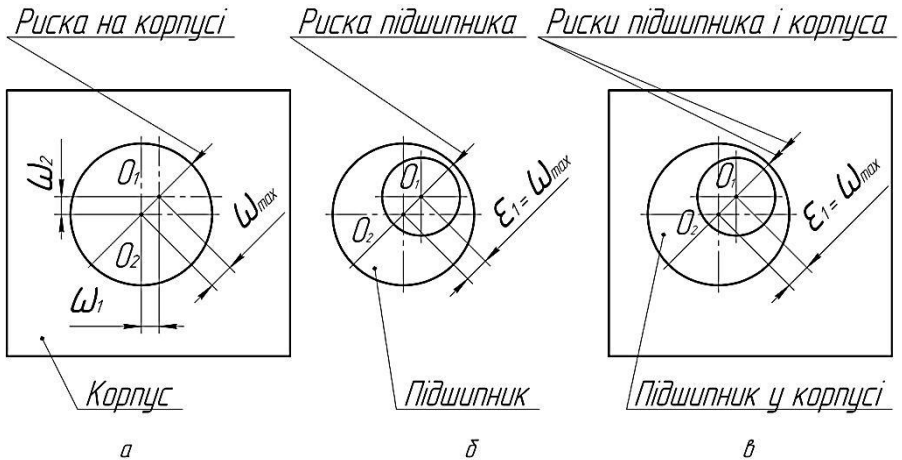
Зменшення похибки повороту осі обертання вала відносно основних баз корпусу
